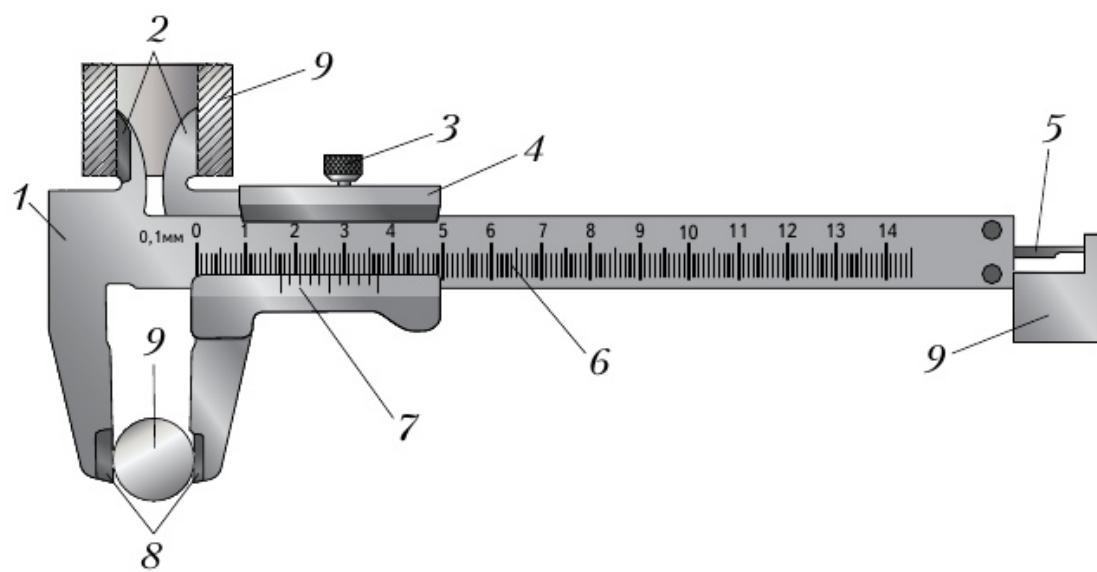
Штангенциркуль ШЦ-1: 1 – штанга; 2 – губки для внутренних измерений; 3 – зажимной винт для фиксации рамки; 4 – подвижная рамка; 5 – глубиномер; 6 – шкала штанги; 7 – нониус; 8 – губки для наружных измерений; 9 – измеряемые детали
